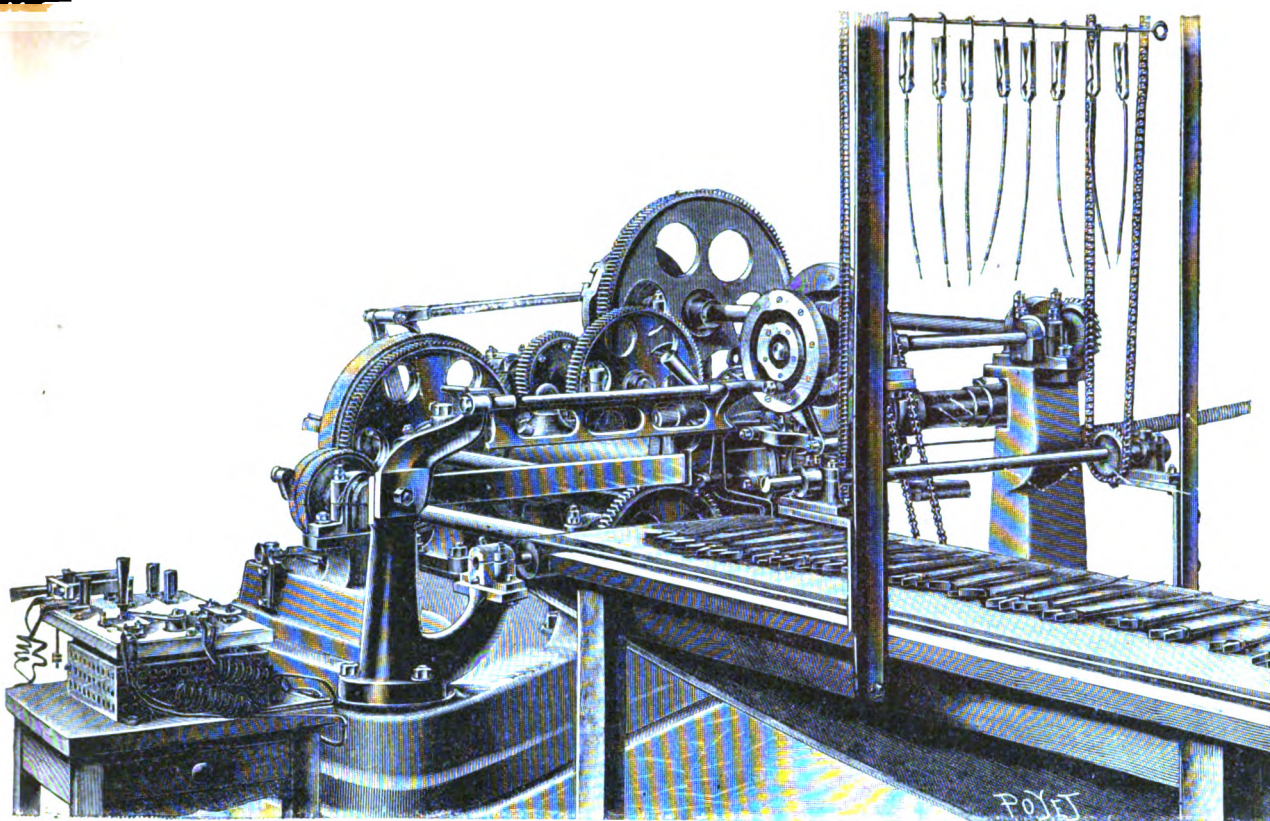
Machine à empâter et à couper les électrodes de longueur.
